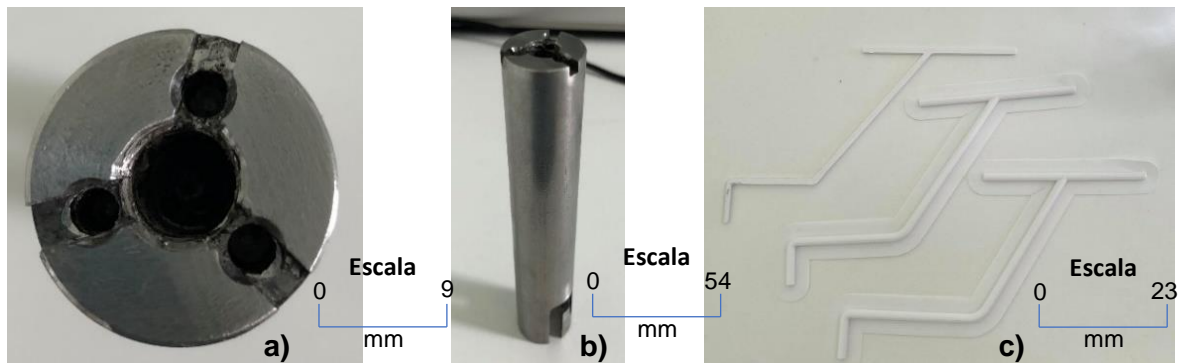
Estrutura do spindle otimizada para três hastes: a) e b) estrutura do spindle produzida e c) impressão 3D das hastes de dimensão M projetadas com diferentes ângulos.
